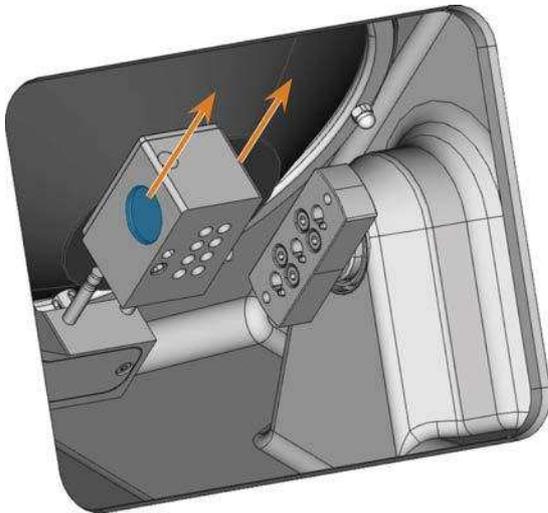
DAS WERKZEUGMAGAZIN HERAUSZIEHEN (LINKE GRIFFMULDE BLAU EINGEFÄRBT)
